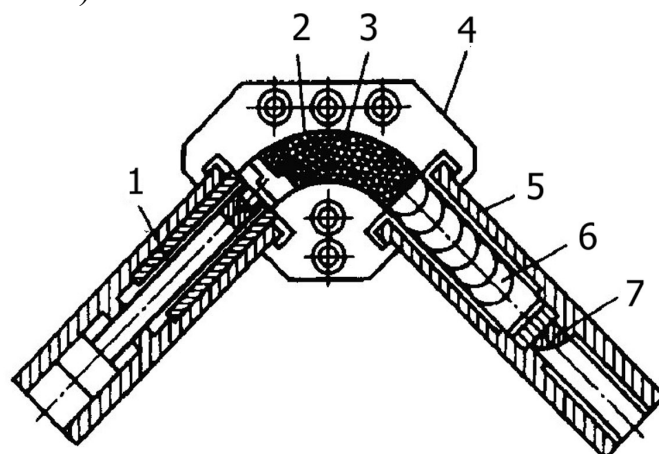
Схема гибки трубной заготовки в жесткой матрице:
